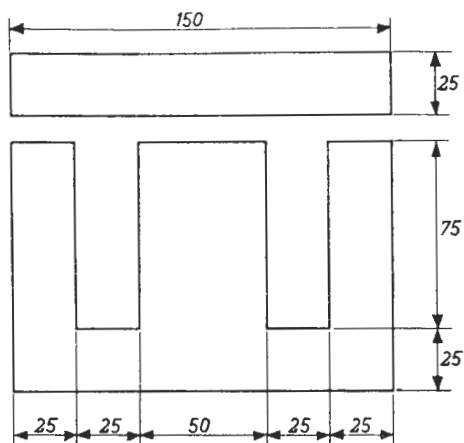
Afmetingen in mm van de lamellen van de uitgangstransformator.
